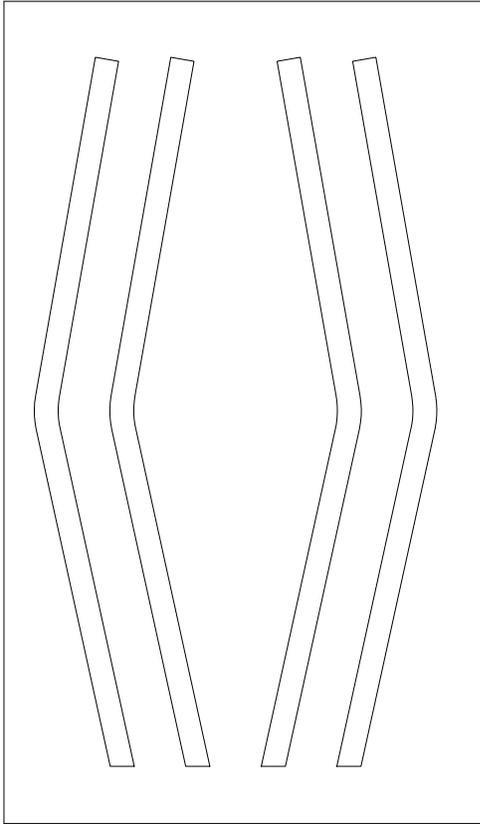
Dessins gabarit usinage : Chaise finale
